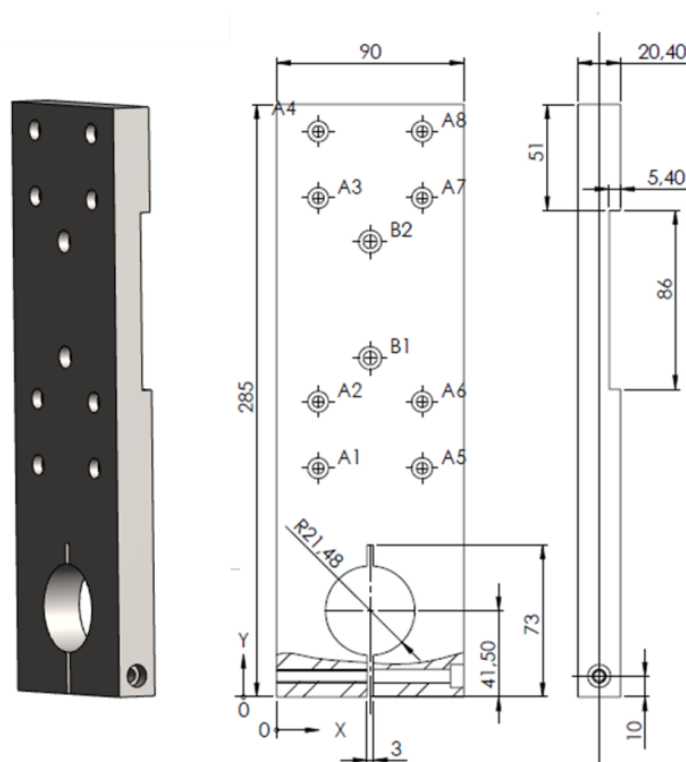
Desenho da placa de suporte da fresa (elaboração própria)
